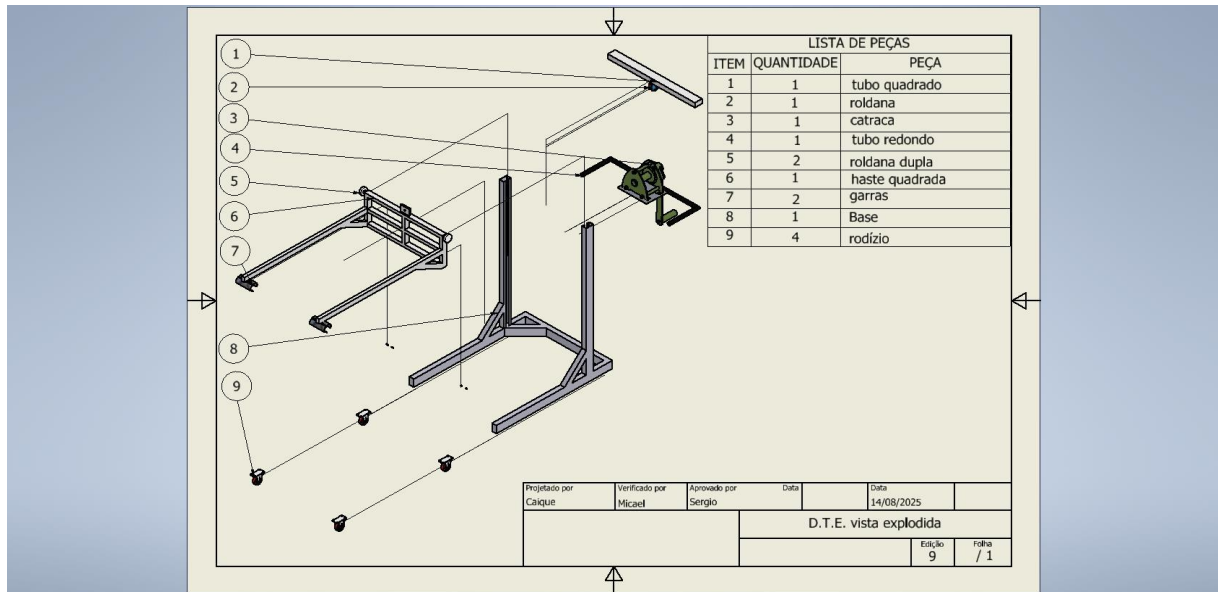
Desenho Explodido - Fonte - Caique Piaia - Inventor autodesk
